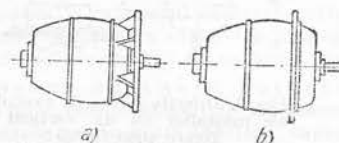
Mașini cu ax orizontal cu fixare prin flanșă: a — flanșă pe scutul port-lagăr; b — flanșă pe carcasă.
